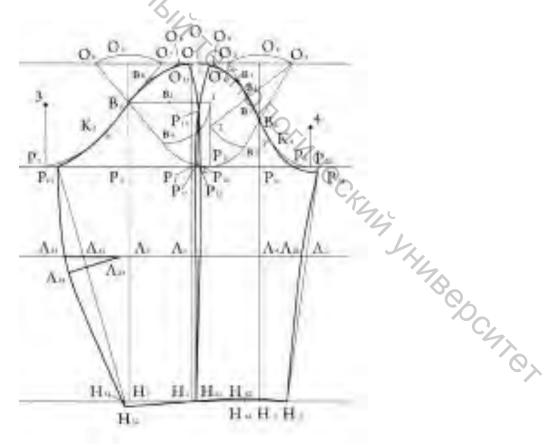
Чертеж базовой конструкции двухшовного рукава со средним швом
